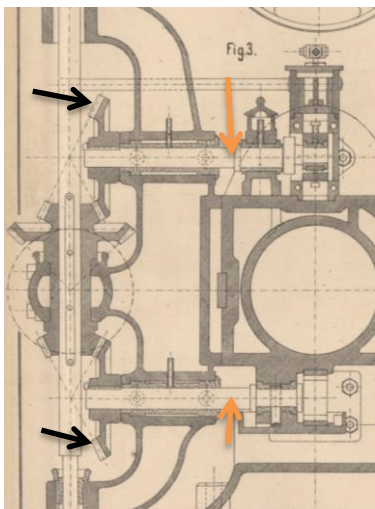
Článek v Polytechnisches Journal r.1879 Obr.173 Regnierův regulátor otáček v řezu
